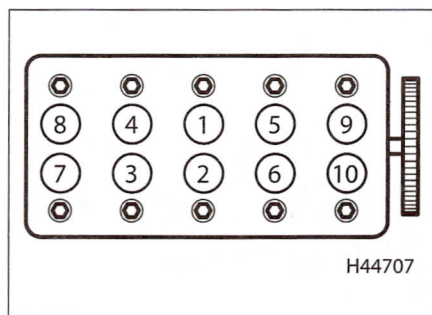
, б. Последовательность затяжки болтов крепления головки цилиндров (двигатели 1.6 л)
